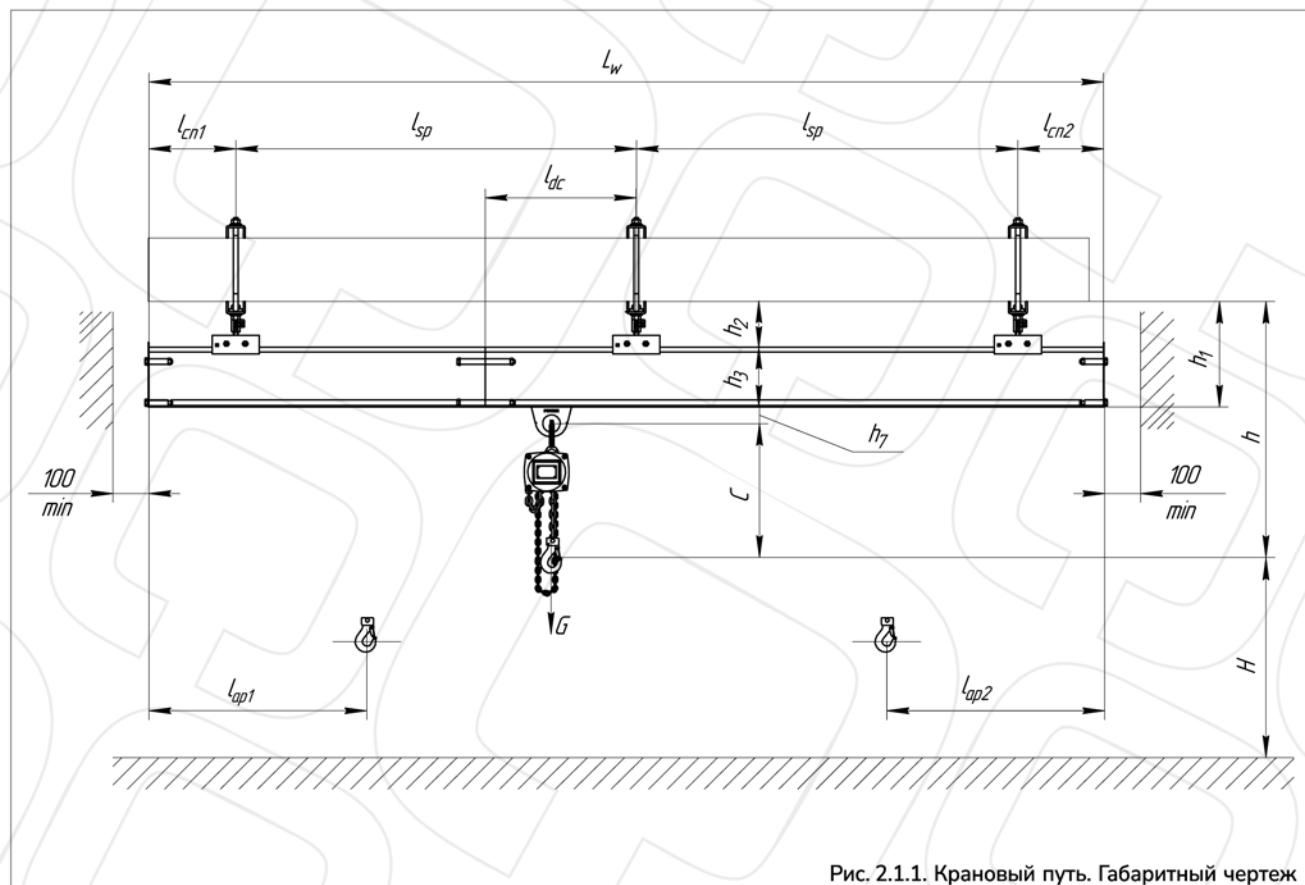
Крановый путь. Габаритный чертеж
